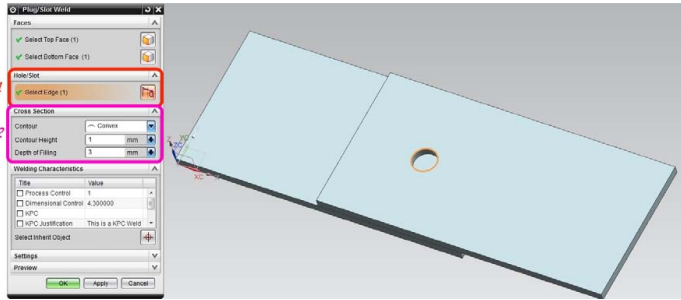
Выбор ребра для сварки и задание размеров пробочного шва
